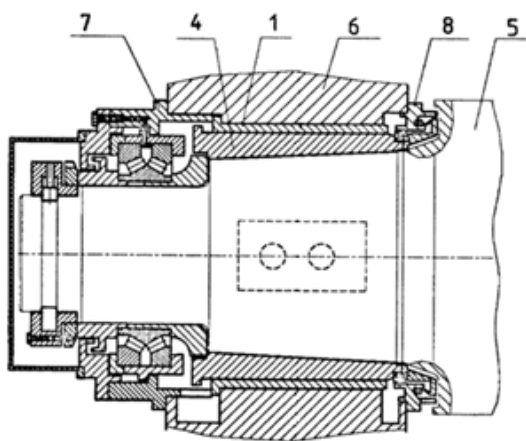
Конструкция подшипникового узла вала прокатного стана [2]
